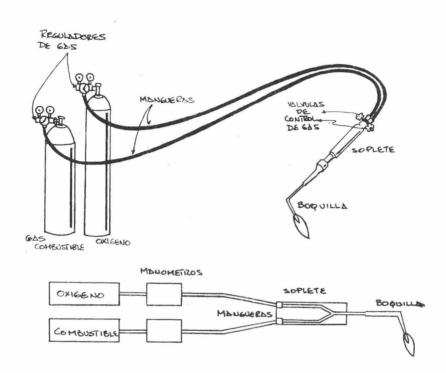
SOLDADURA CXIACETILENICA.
